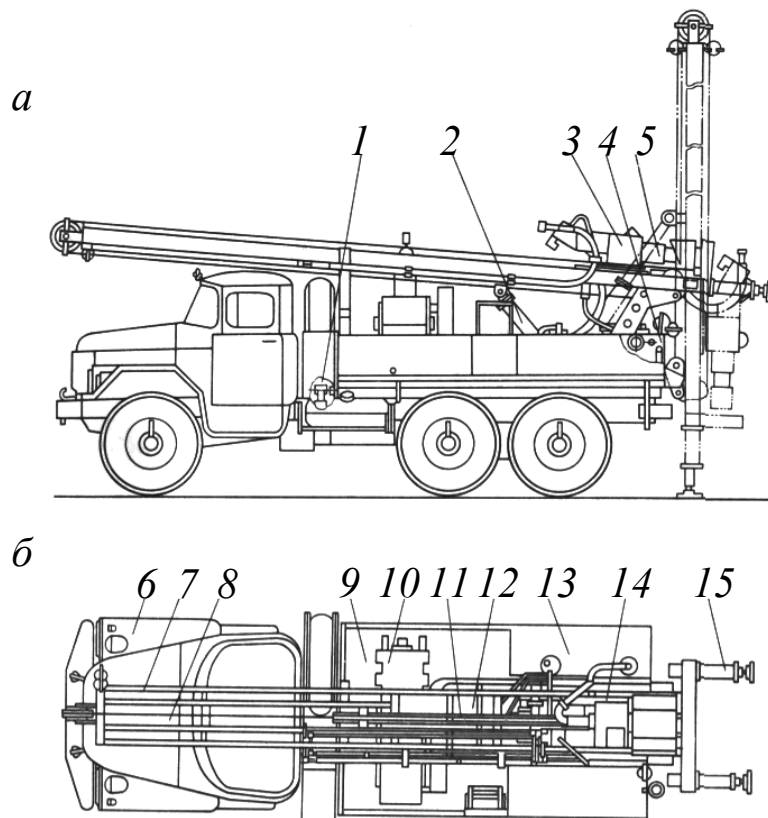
Буровая установка УРБ-2А-2: *а* – вид сбоку; *б* – вид сверху; 1 – коробка отбора мощности; 2 – цилиндр подъема мачты; 3 – вращатель; 4 – пульт управления; 5 – элеватор для труб и патрон для шнеков; 6 – автомобиль; 7 – мачта; 8 – талевая система; 9 – рама; 10 – установки бурового насоса и компрессора; 11 – гидродомкрат подачи; 12 – раздаточная коробка; 13 – обвязка гидросистемы; 14 – каретка; 15 – опорный домкрат
